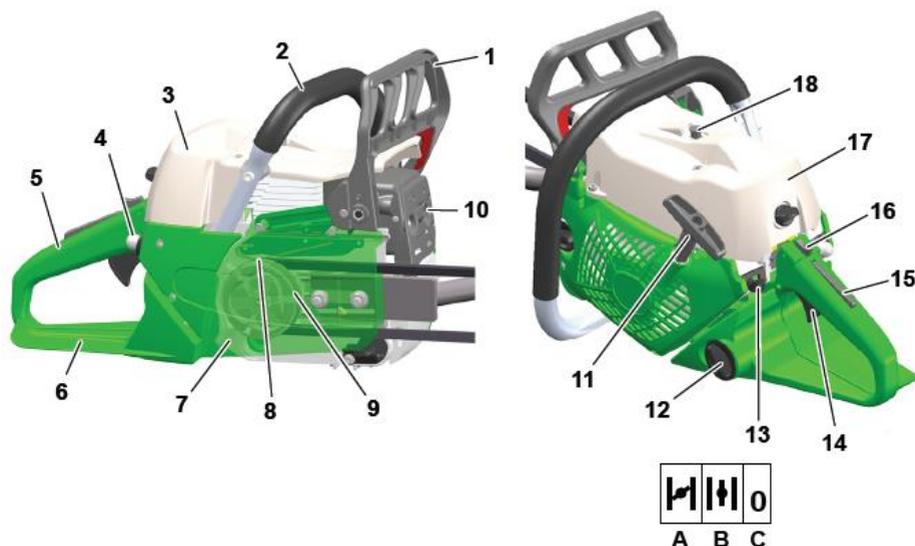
Vue d'ensemble du moteur d'entraînement
